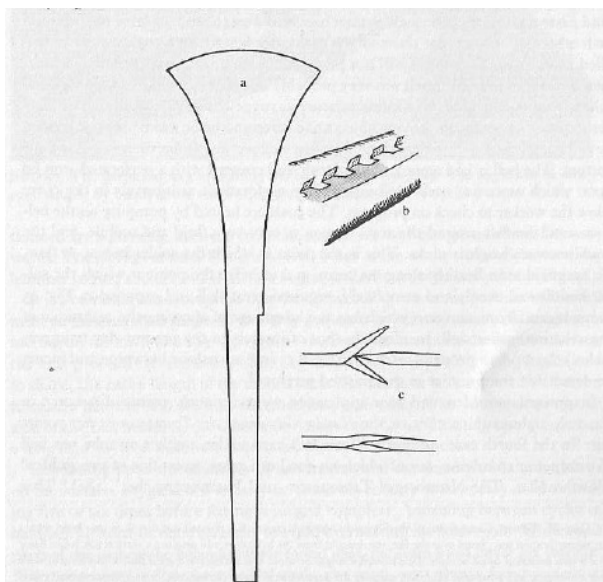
Dibujo de una plantilla y su ensemble.
